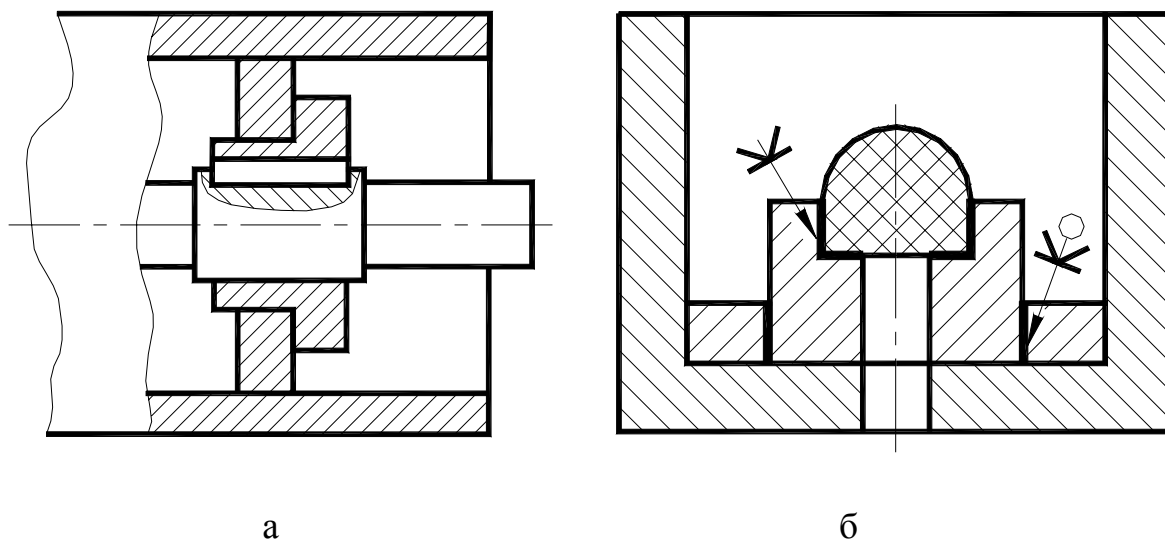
Изображения сварного (а) и клееного (б) соединений в сборе с другими изделиями на чертежах общего вида
